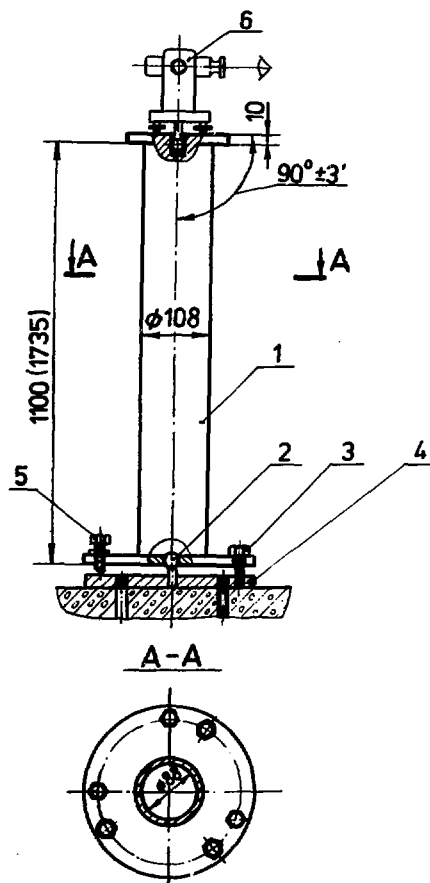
Тумба для установки геодезических приборов: 1 - тумба; 2 - шарик установочный; 3 - болт крепежный; 4 - подставка; 5 - болт юстировочный; 6 - геодезический прибор.
